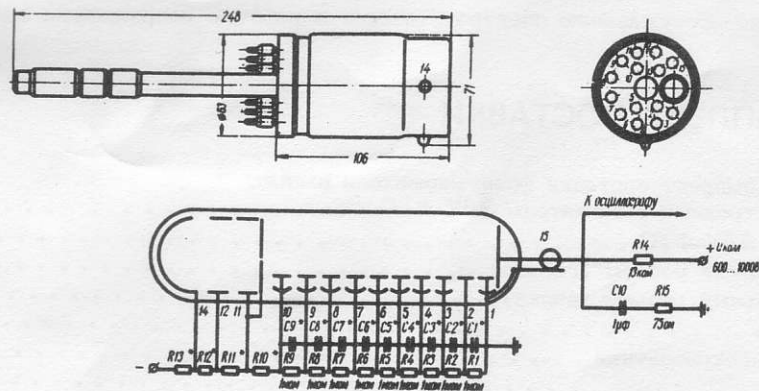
Габаритные размеры, цоколевка и схема включения прибора типа ЭЛУ-ФТС ($n = 9$);
